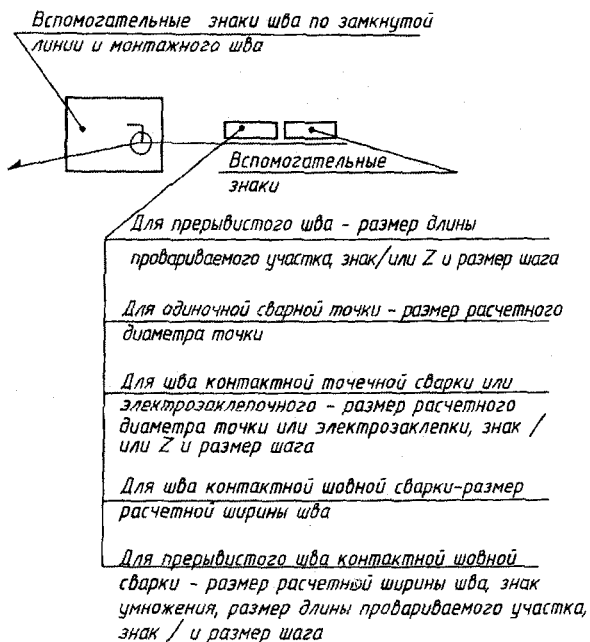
Структура условного обозначения нестандартного шва или одиночной сварной точки
